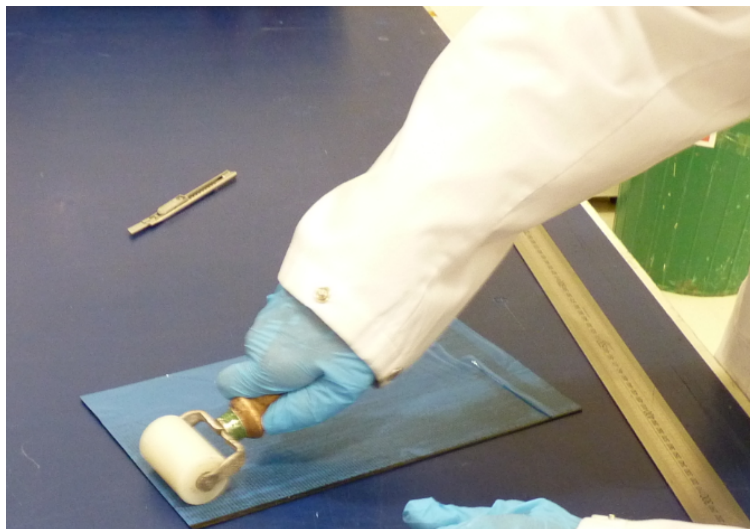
Realización del laminado con ayuda de un rodillo.
